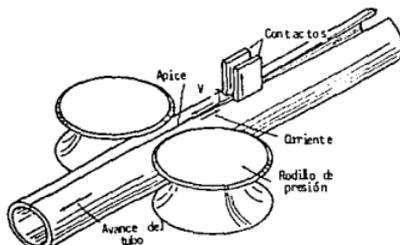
Método para hacer una soldadura en costura en tubo mediante una corriente de alta frecuencia como el medio de calor.
